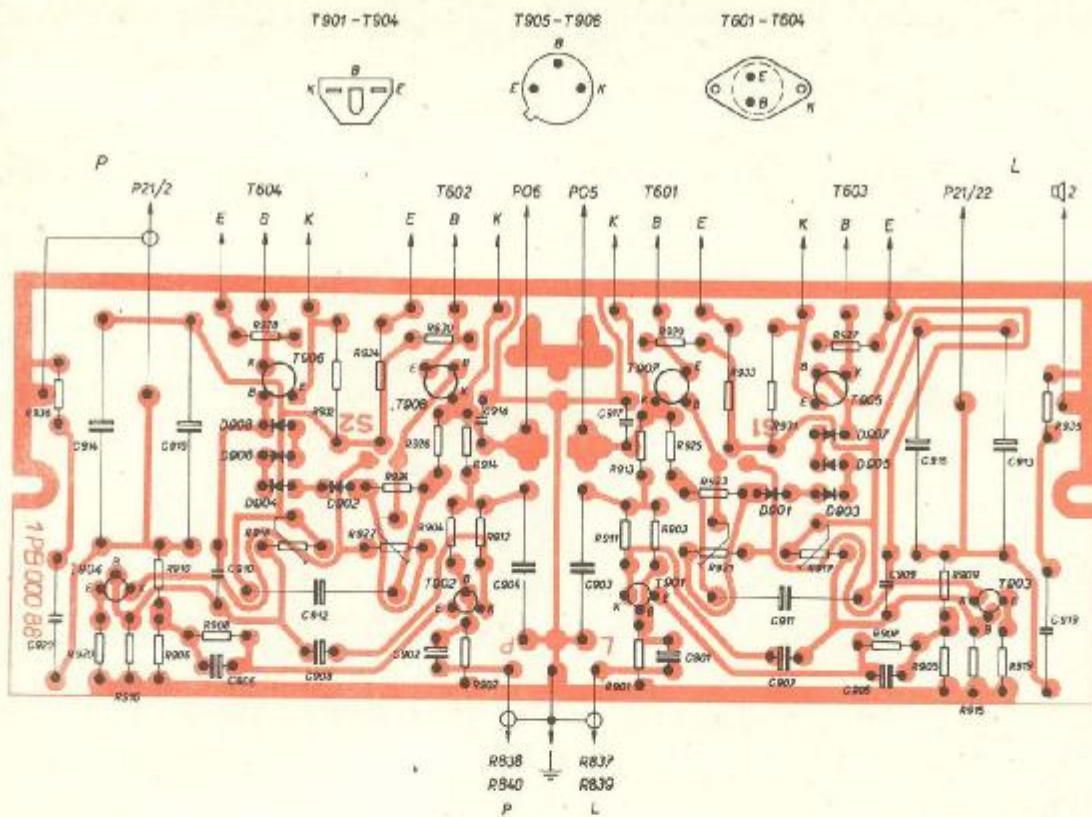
Montážní zapojení předzesilovače pro přenosku
